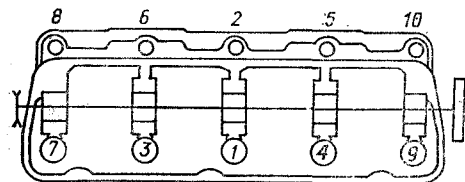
Порядок затяжки болтов крепления головки блока цилиндров
